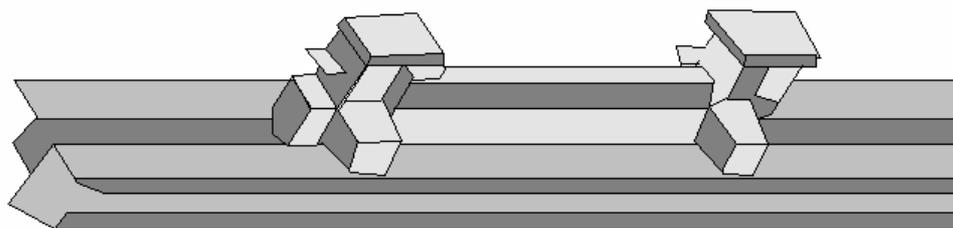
Mitad del carro móvil del sistema de Guías Deslizantes/Elaboración
